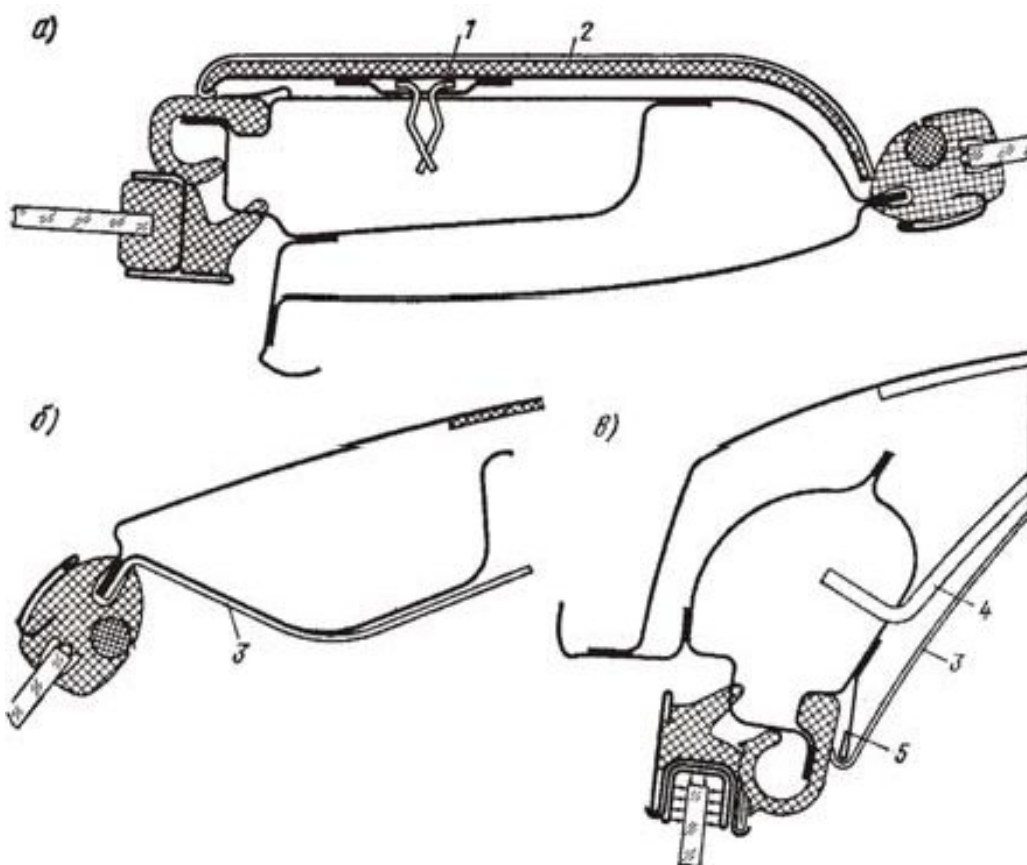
Крепление обивки задней части боковины и обивки потолка:
